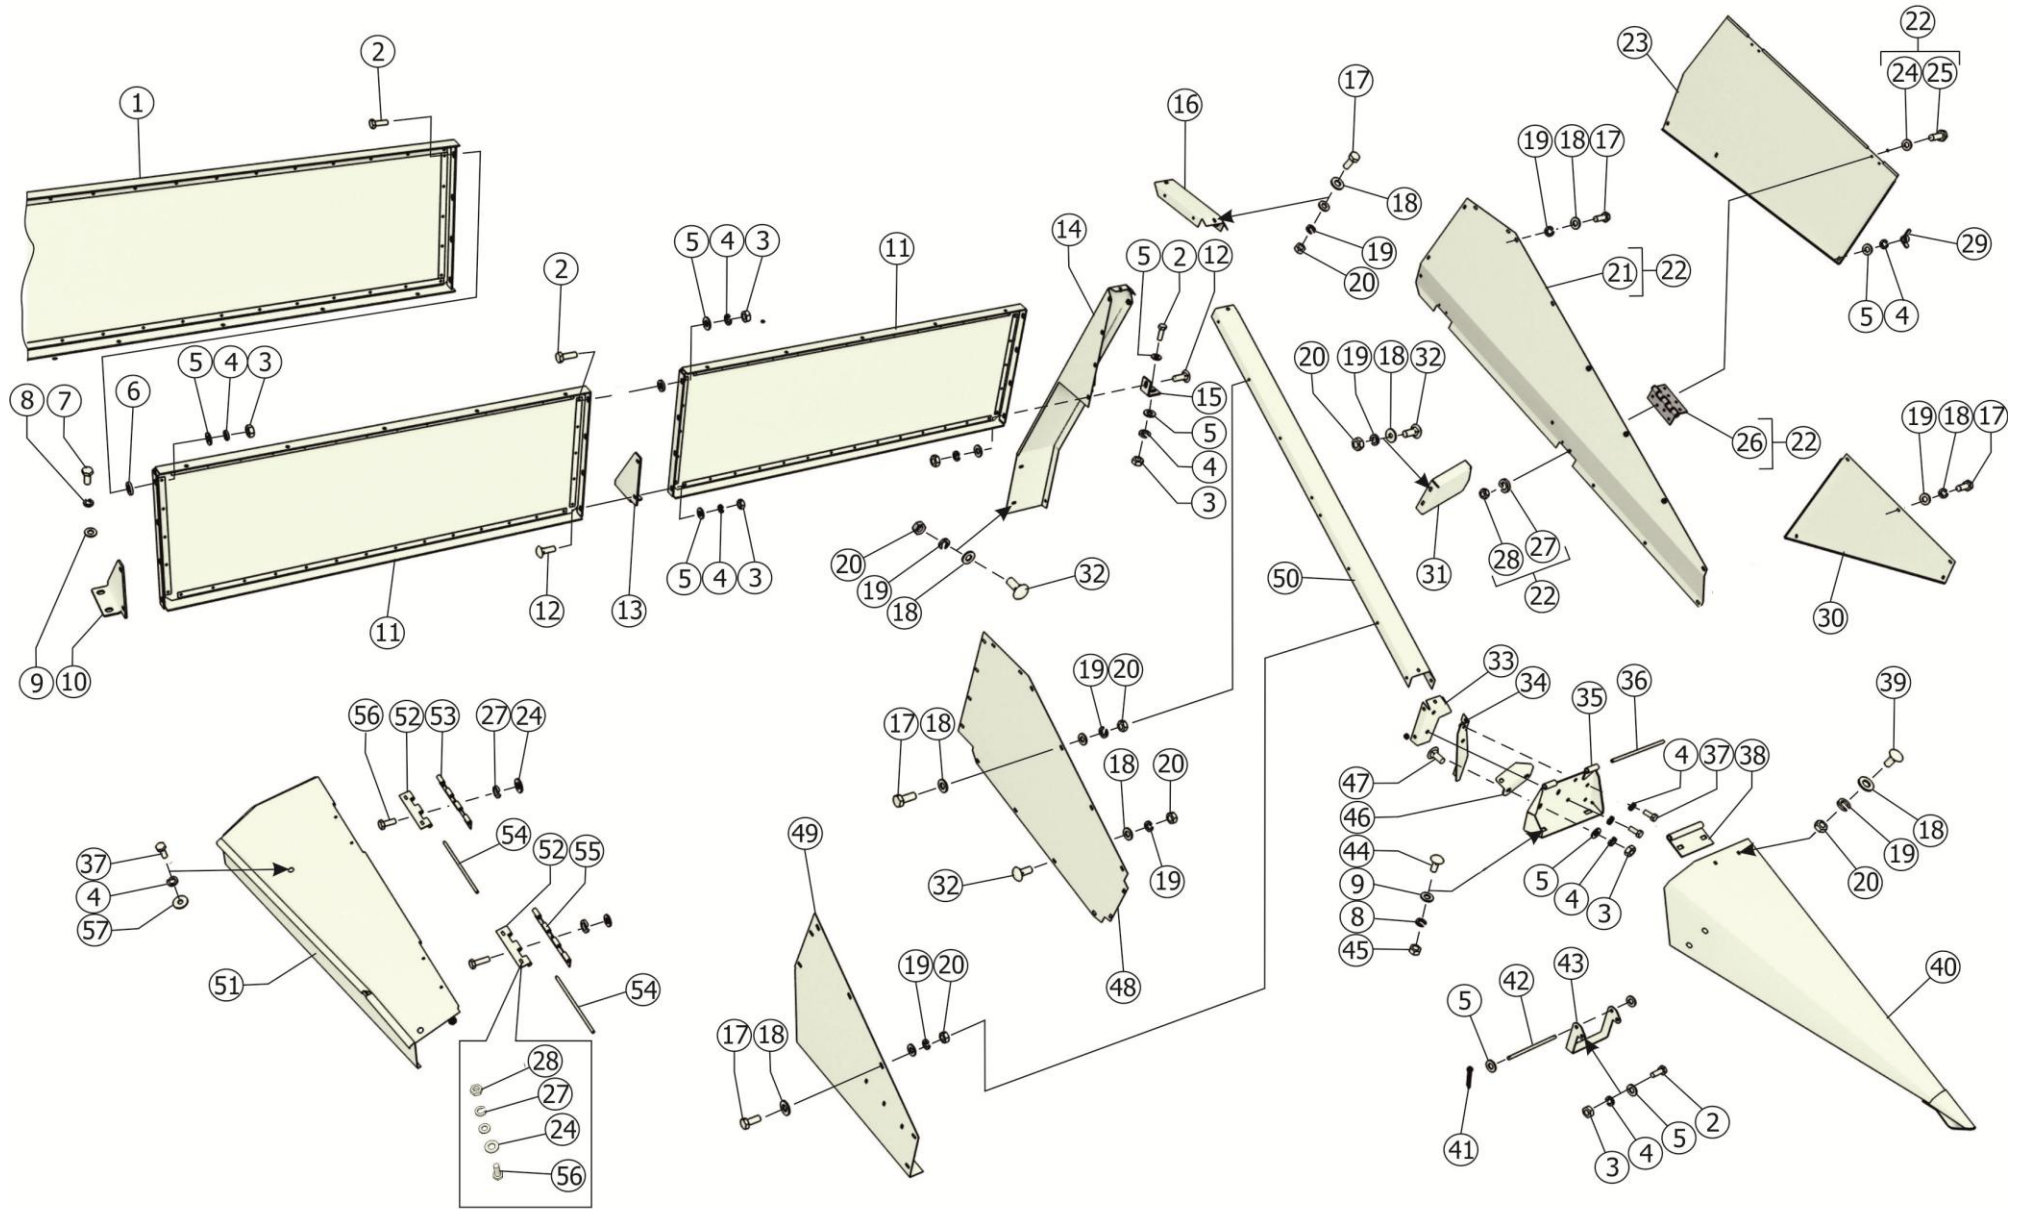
Установка щитов ПСП-1210.01.11.000А. Вид слева
